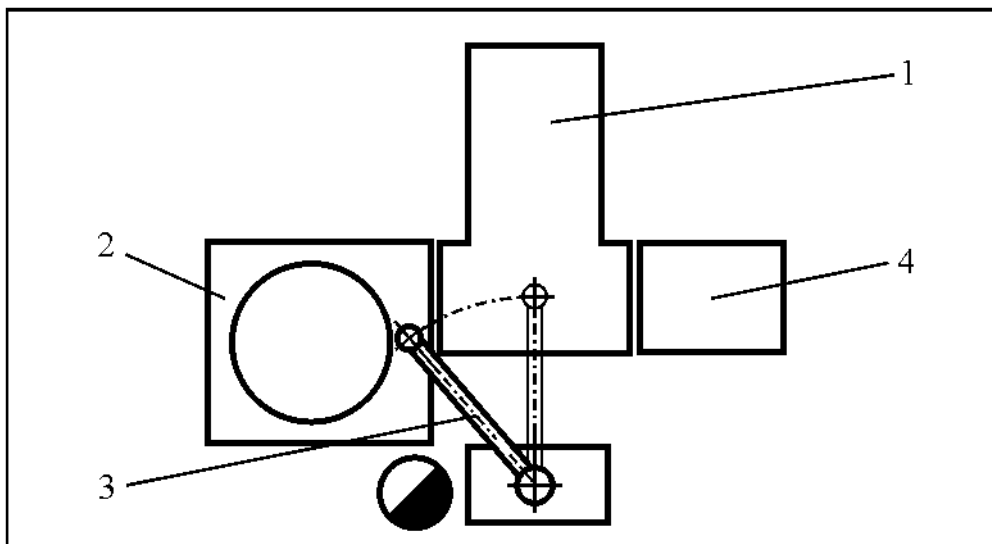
План-схема організації робочого місця оператора, що обслуговує роботизований штампувальний комплекс для роботи від штучної заготовки: 1 - кривошипний відкритий прес; 2 - автоматизований бункерний завантажувально-орієнтовочний пристрій; 3 - маніпулятор; 4 - бункер для деталей
